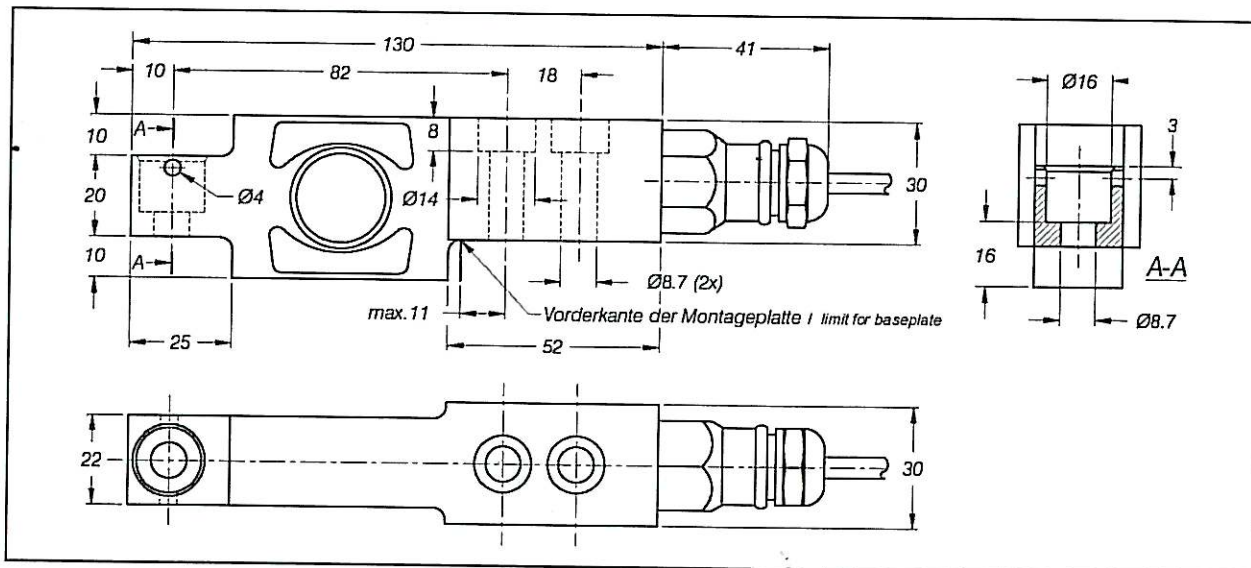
Abmessungen der Wägezelle Typ SB6 / Figure 2: Dimensions of the load cell type SB6
